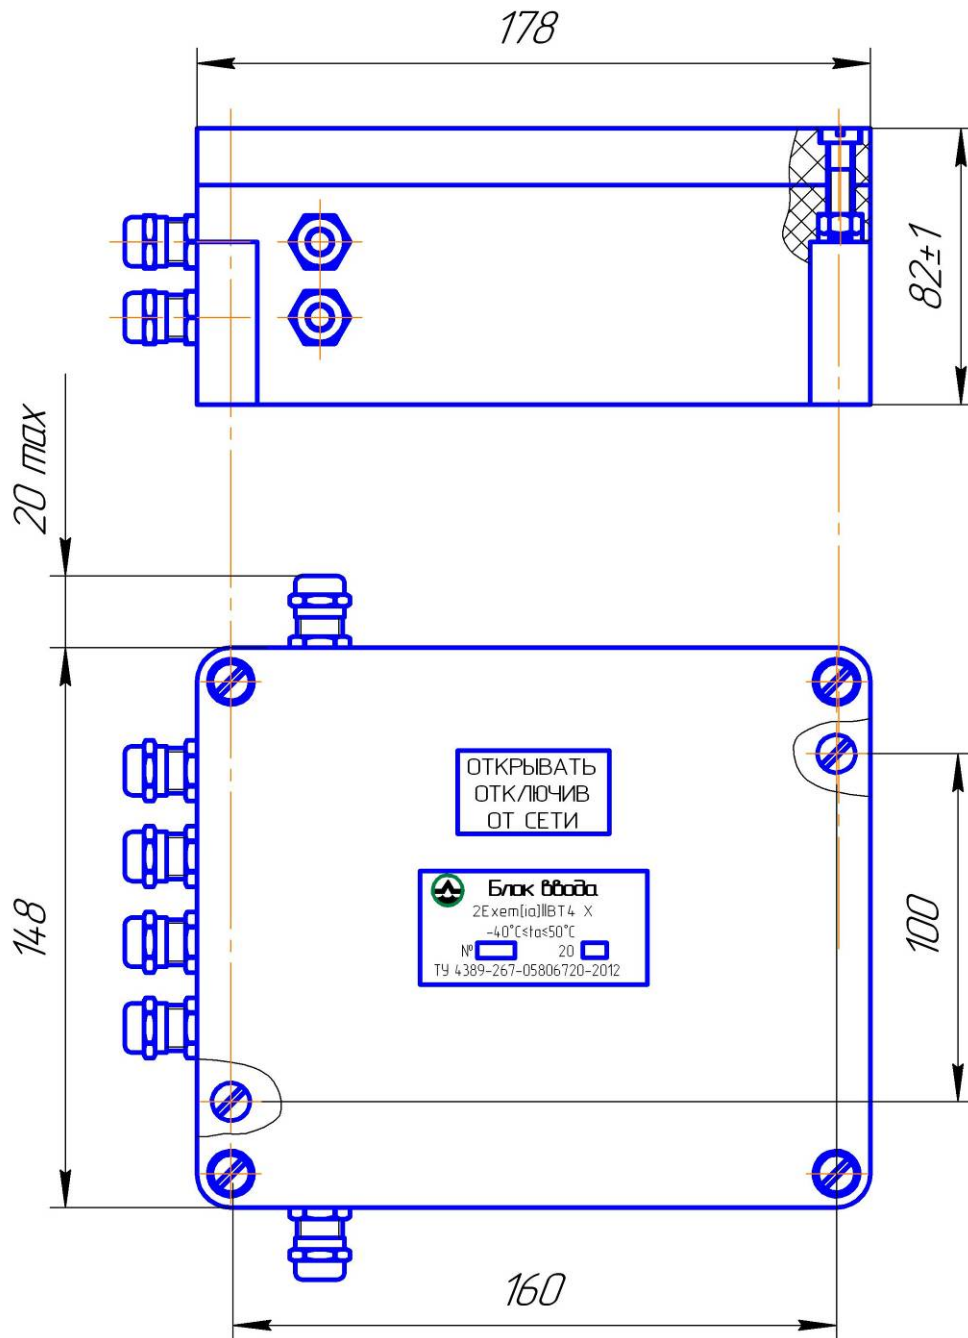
БВ. Габаритные и присоединительные размеры
